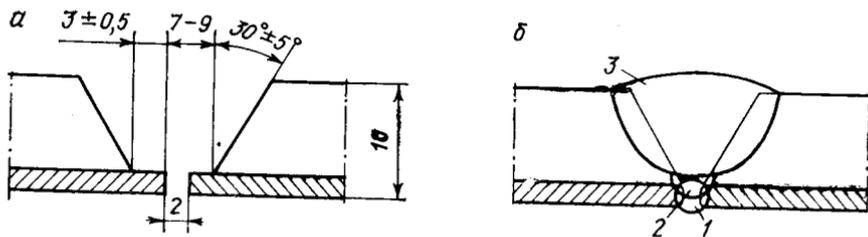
Разделка кромок (а) и нанесение сварочных слоев (б) при сварке двухслойных сталей:
